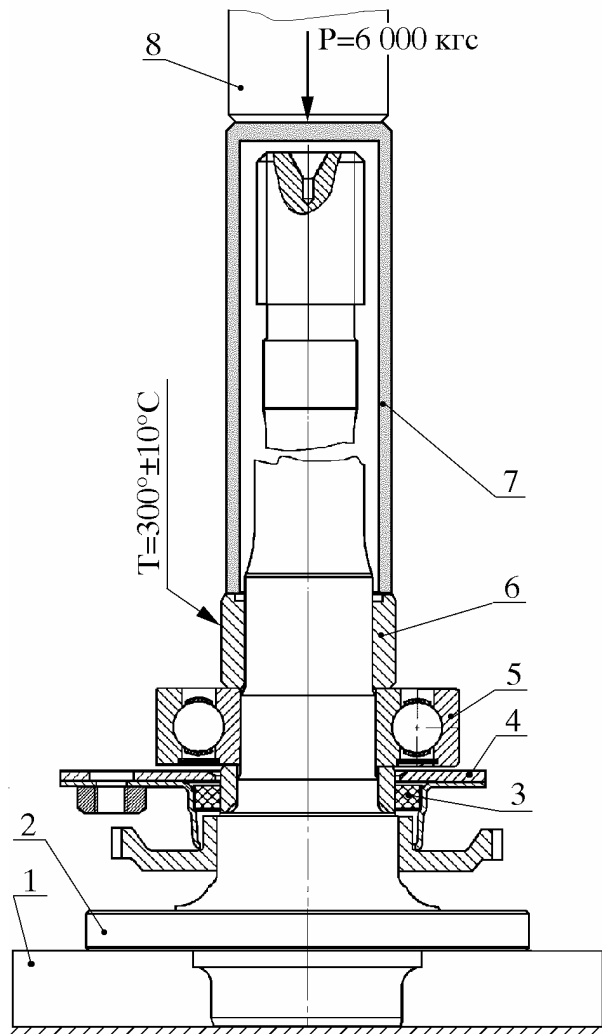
Напрессовка подшипника и запорного кольца на полуось:
